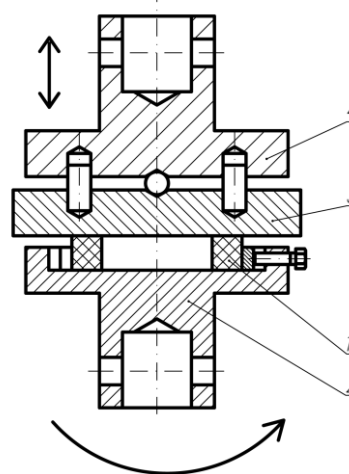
Приспособление для исследования изнашивания: 1 – кольцевой образец; 2 – захват; 3 – контртело; 4 – самоустанавливающийся захват
